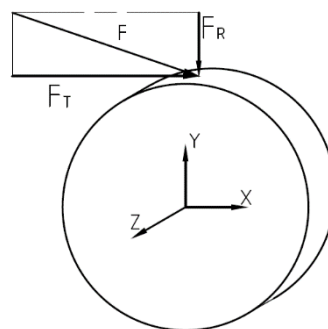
Fuerzas que actúan sobre engranajes de dientes rectos
